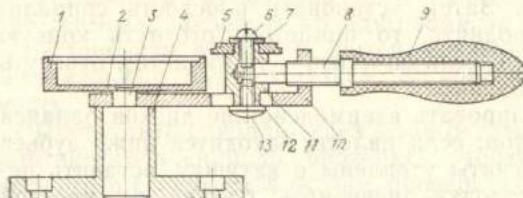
Приспособление для закатывания ободка в часах «Луч» 38181:
